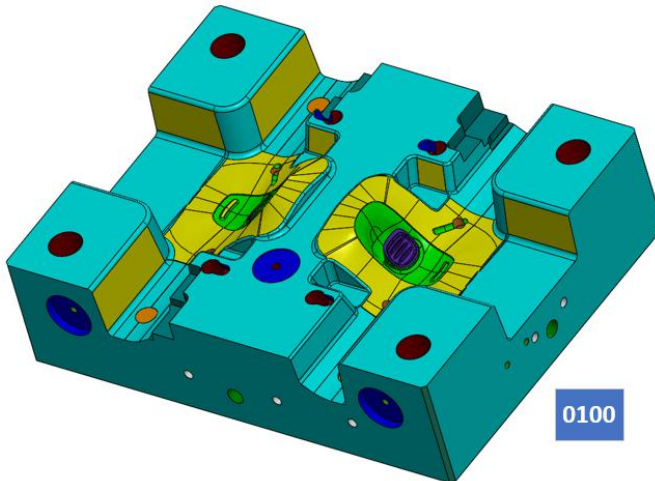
Placa moldante, lado da injeção em vista isométrica
